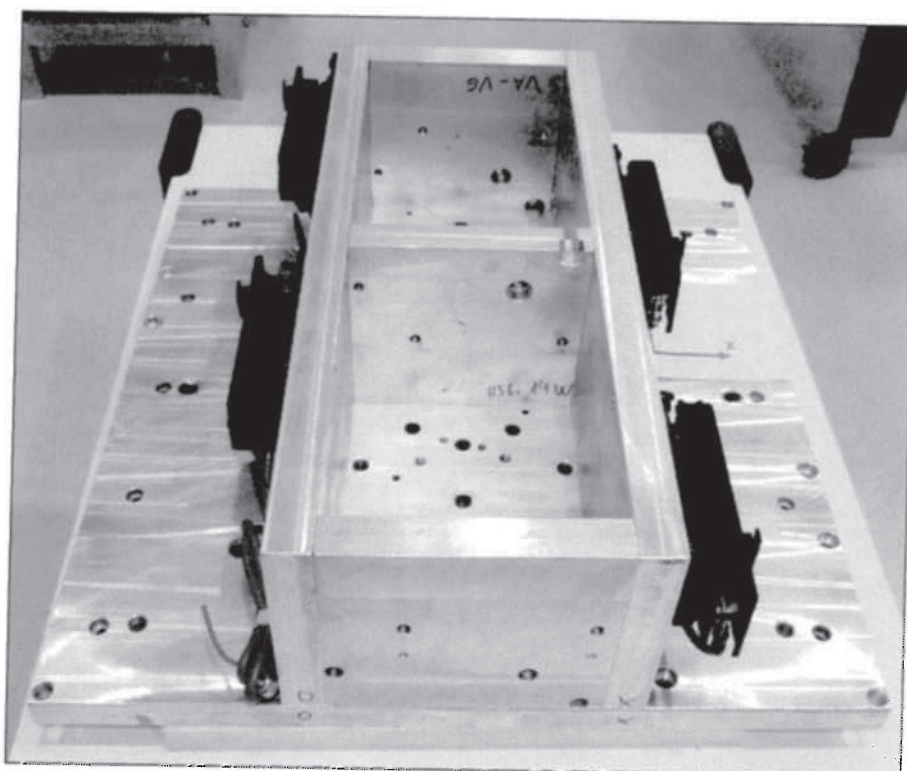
Vista geral com Amostras #01, #02, #03 e #04 montadas no adaptador de vibração.
